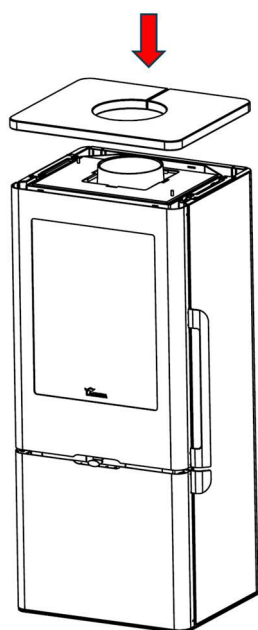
Étape 10. Installer le dessus en pierre serpentine
